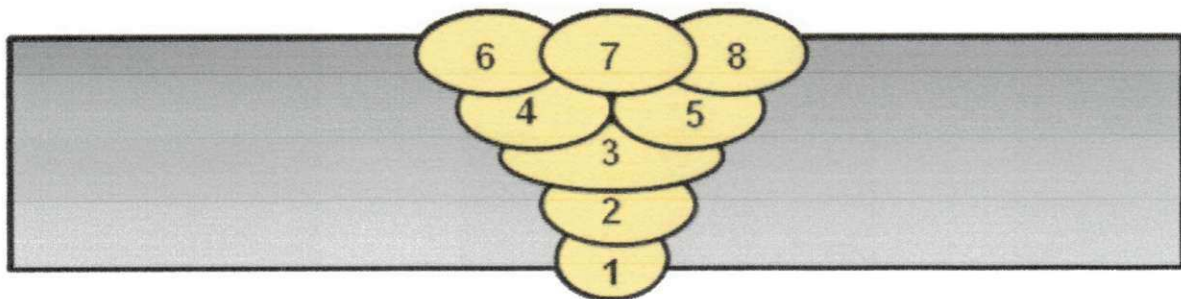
Aspecto final e seqüência de passes de soldagem.
